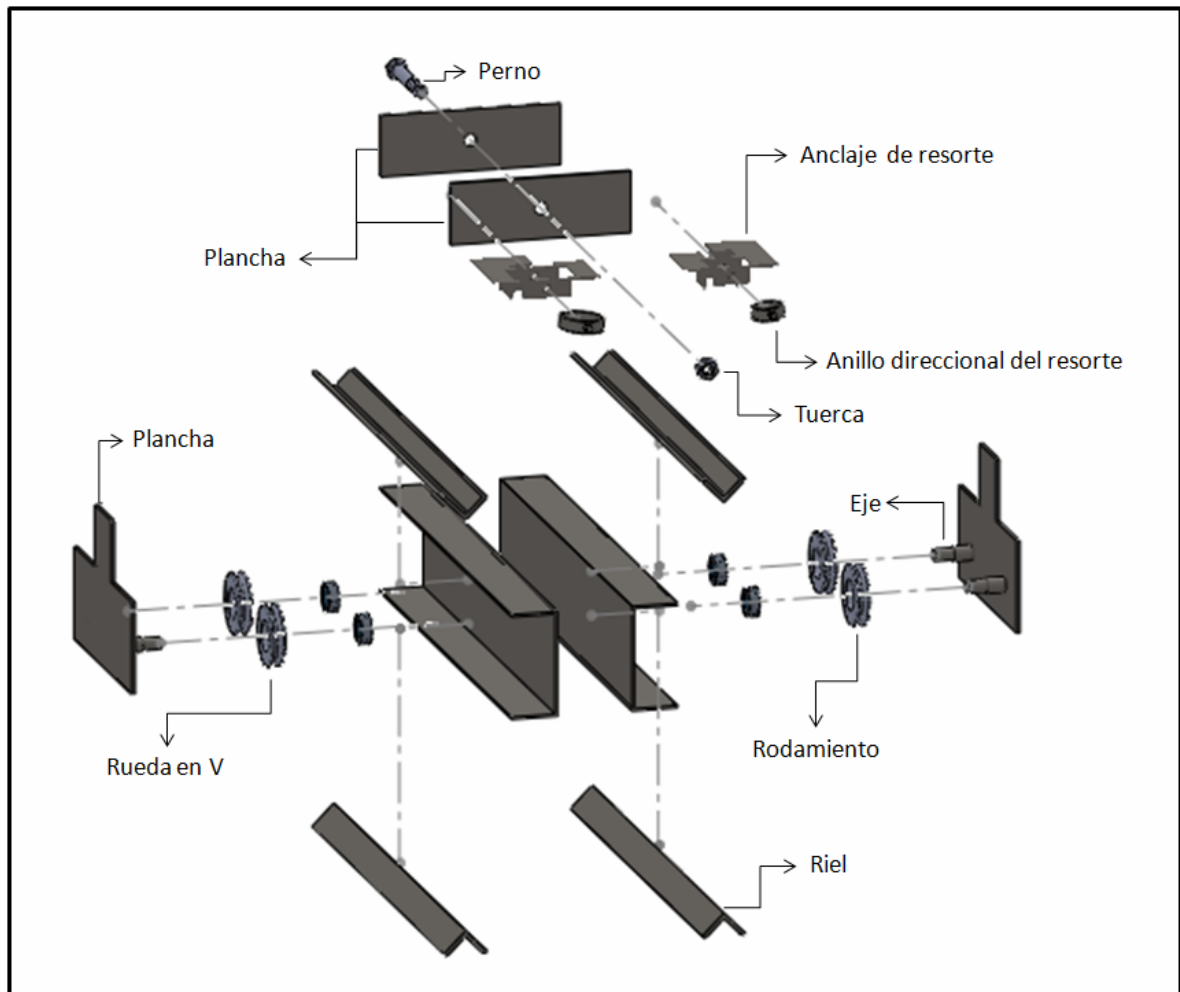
Despiece del carro del mecanismo de desplazamiento [Fuente: propio].
